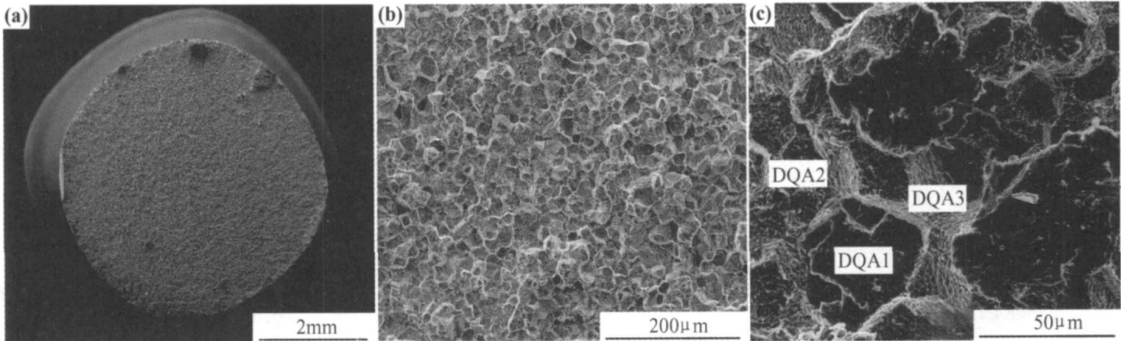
1[#] 工艺 A[#] 钎料钎焊接头拉伸断口形貌
